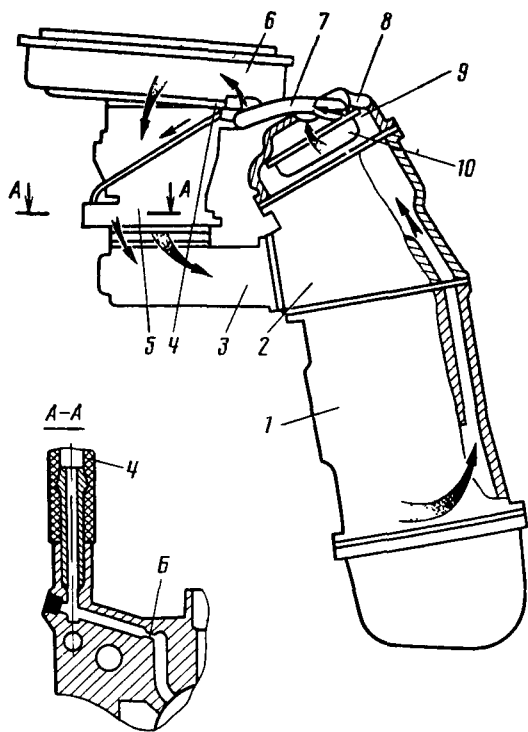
Схема системы вентиляции картерных газов: 1 — блок цилиндров; 2 — головка цилиндров; 3 — впускной коллектор; 4 — трубка отсоса картерных газов в карбюратор; 5 — карбюратор; 6 — воздушный фильтр; 7 — шланг вентиляции картера; 8 — прокладка; 9 — крышка головки цилиндров; 10 — маслоотражатель; Б — калиброванное отверстие диаметром 1,5 мм
